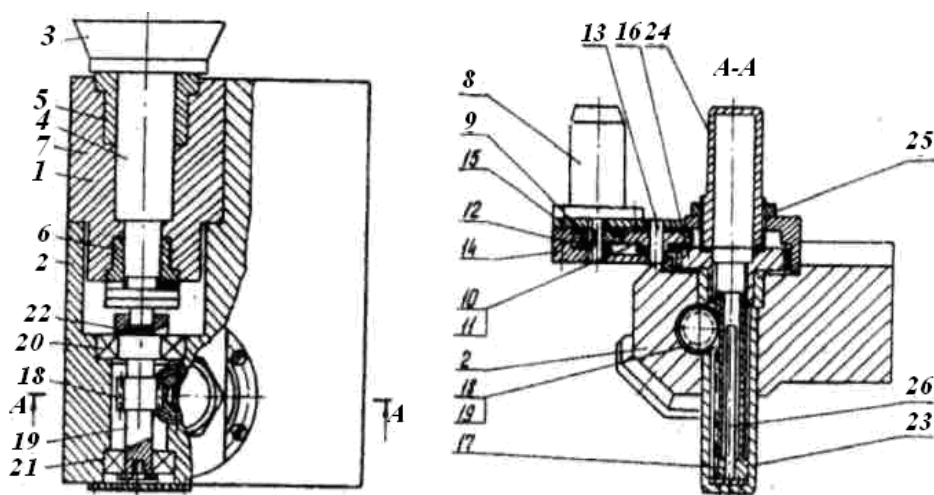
Эскиз резца с принудительным обновлением режущей кромки
